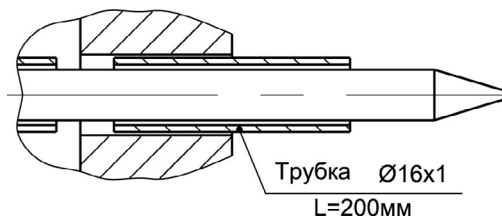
Направляющий стержень для выемки трубки из трубной доски
